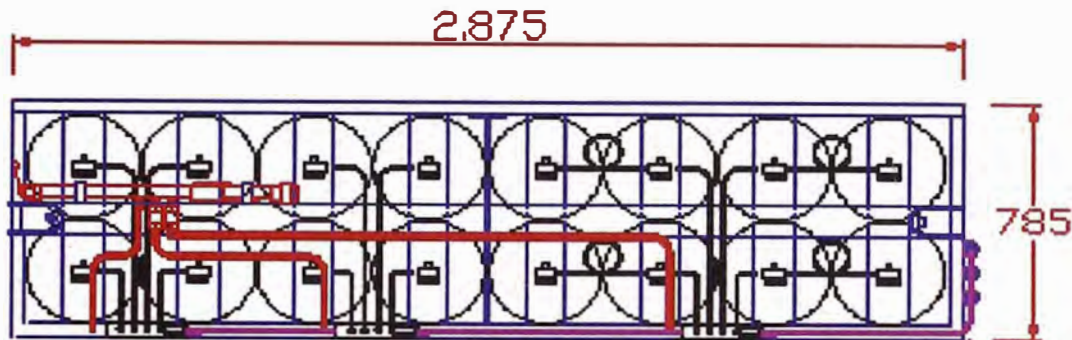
Vista en planta del módulo de almacenamiento de gnv
